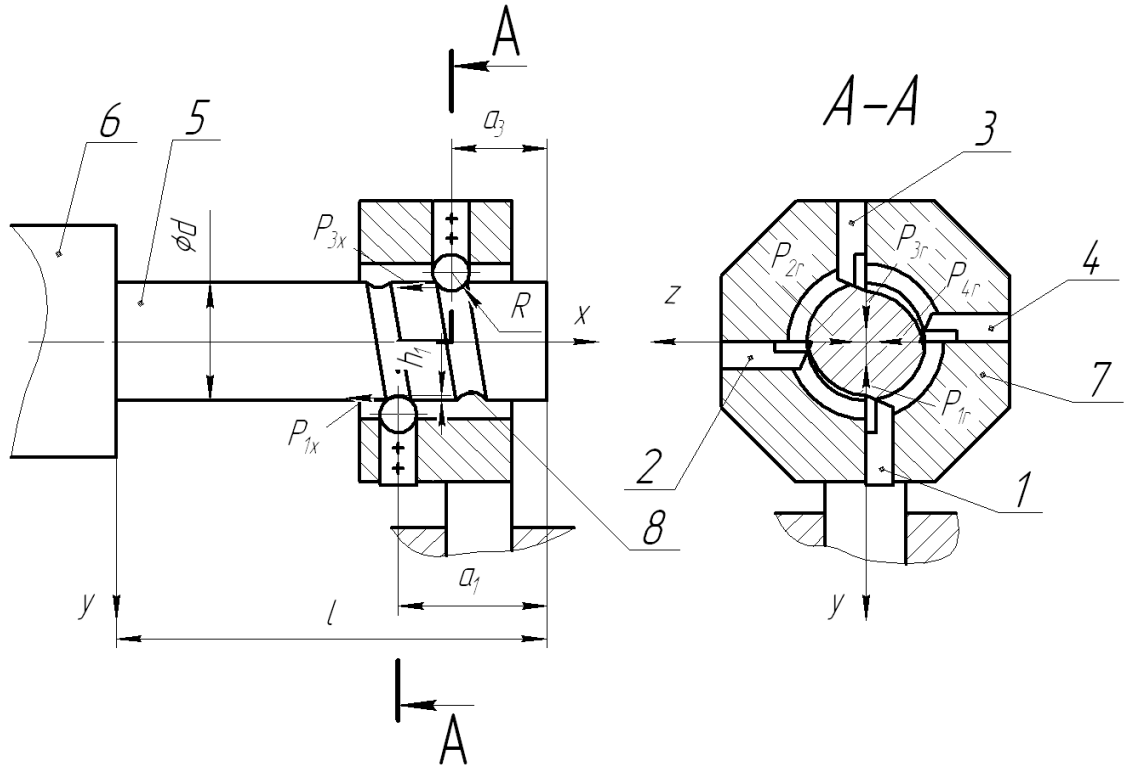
Розрахункова схема для визначення деформації заготовки в процесі нарізання зовнішніх радіусних канавок чотирма різцями одночасно: 1, 2, 3, 4 – радіусні канавочні різці; 5 – заготовка; 6 – патрон; 7 – пристрій для нарізання канавки; 8 – зовнішня радіусна канавка
